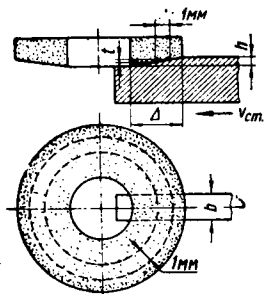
Схема расположения шлифовального круга и детали при обдирке плоскостей.
